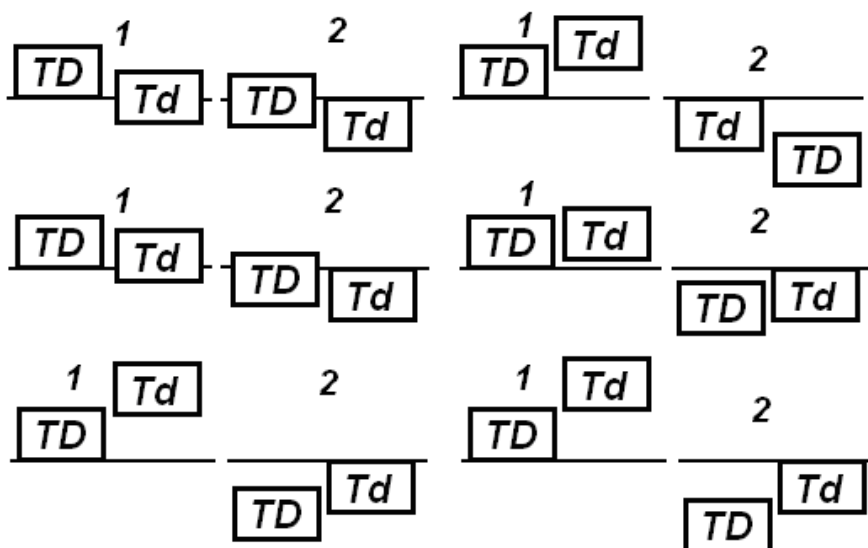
Схеми розташування полів допусків до задачі 46.
